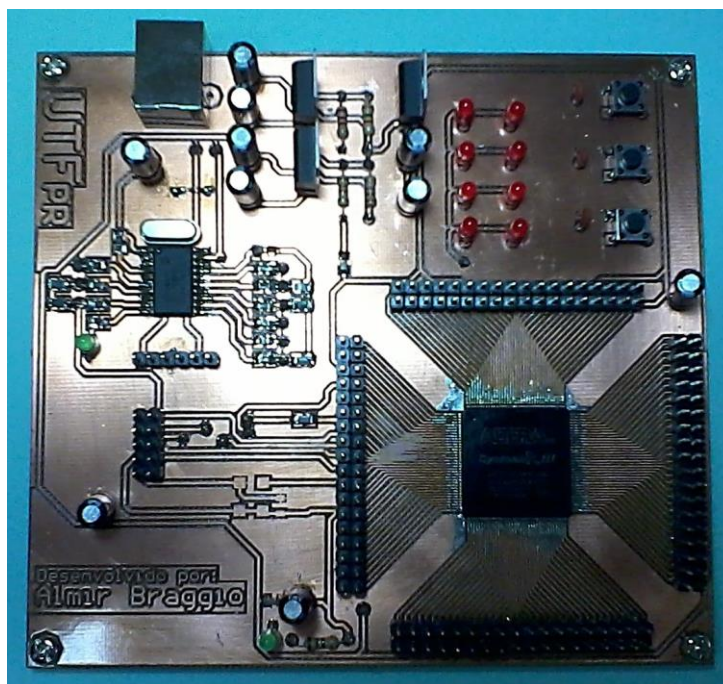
Vista Superior PCB (12.4 cm x 11.35 cm)
